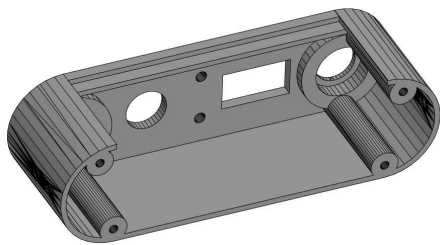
3D-модель корпусу прототипу робота-розвідника
